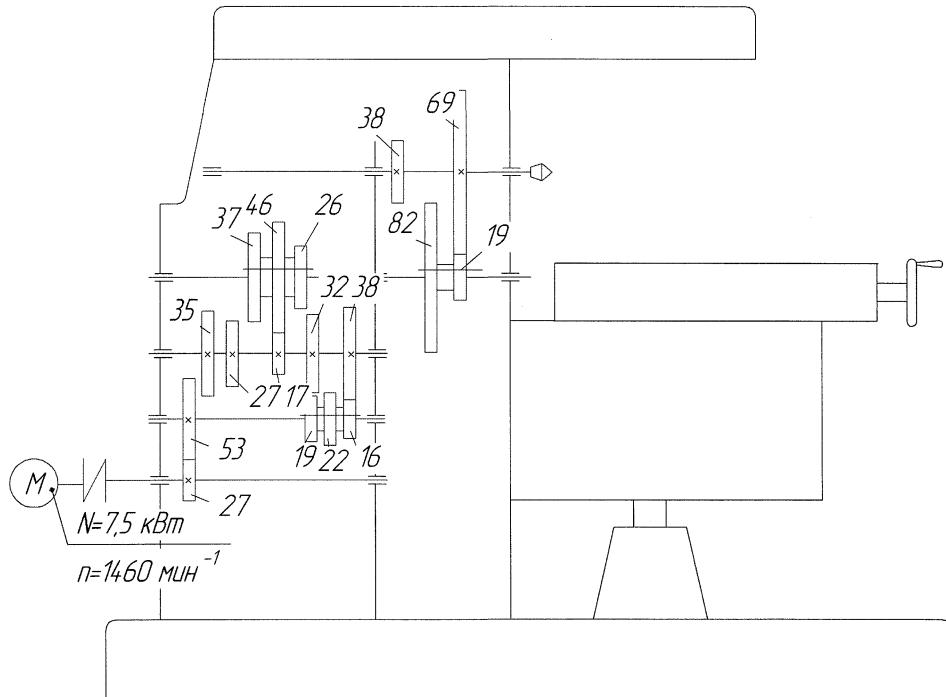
Кинематическая схема коробки скоростей станка 6Р82
